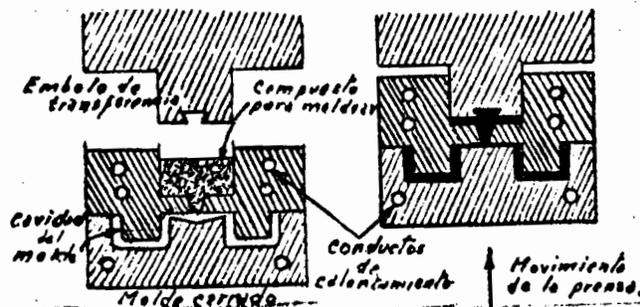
MOLDEO POR TRANSFERENCIA.
